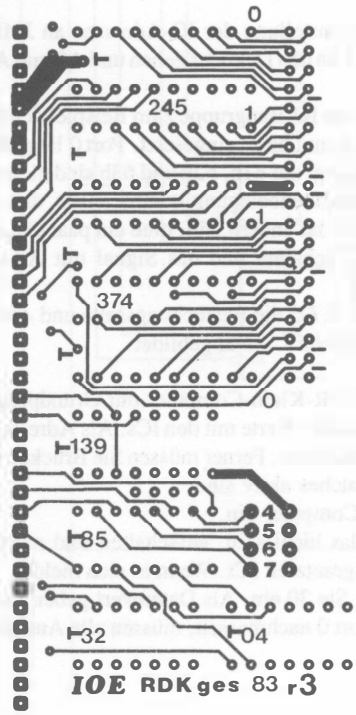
(links) Die Bestückungsseite der IOE-Baugruppe
